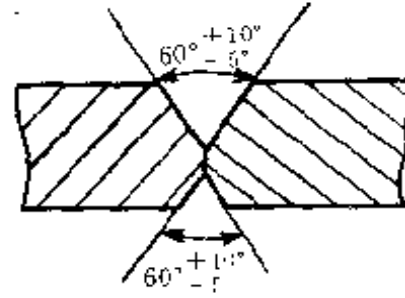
H型钢厚板对接埋弧焊的坡口尺寸
